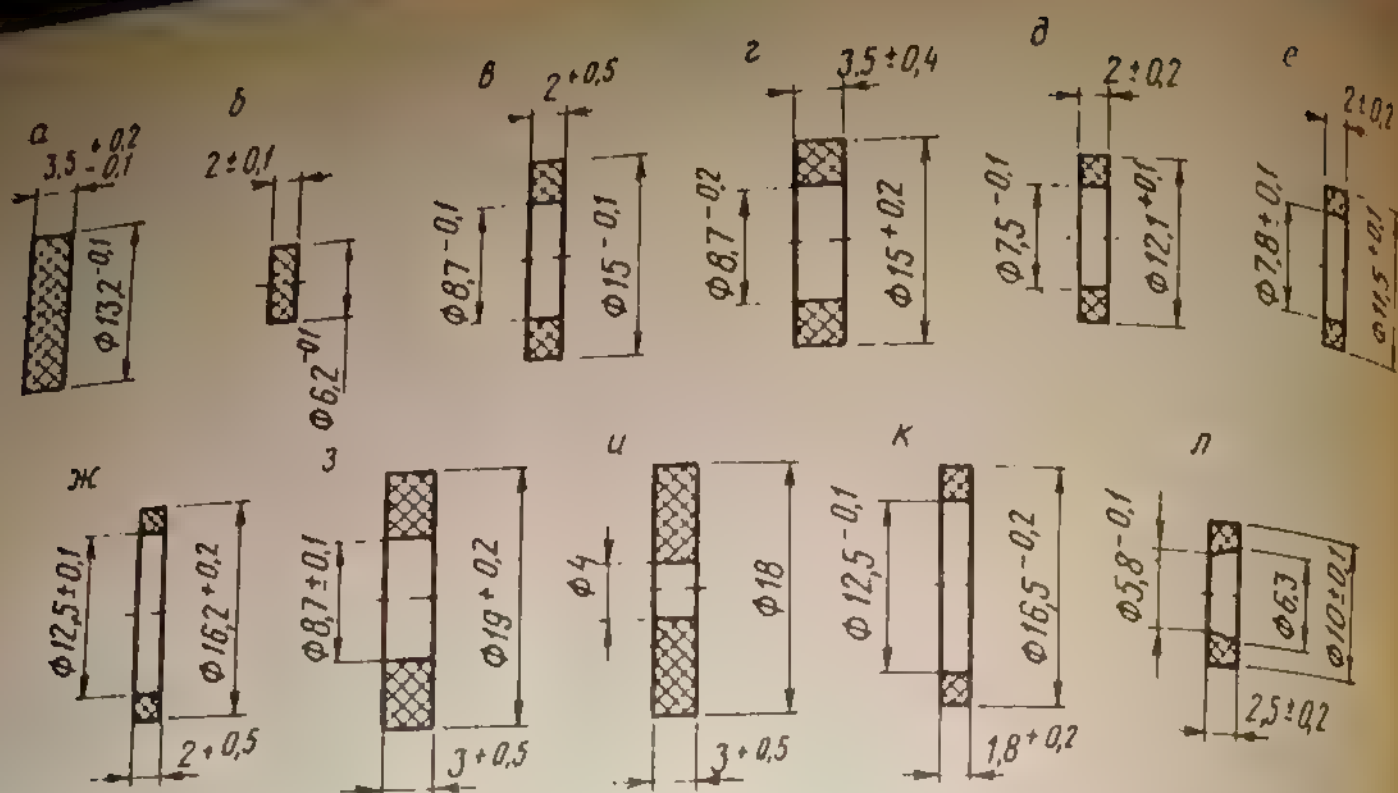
Резиновые изделия, изготовленные с помощью пресс-вырезки
